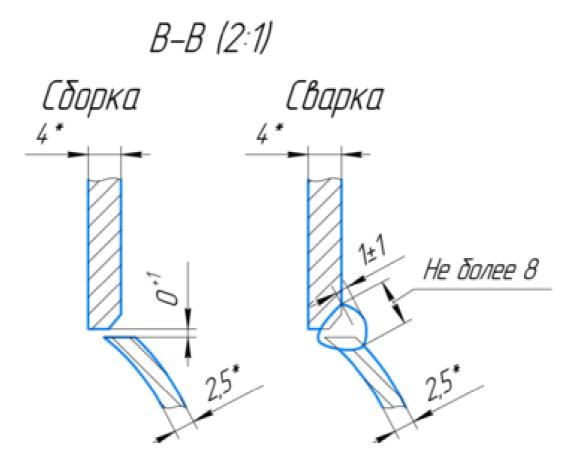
Общий вид шва, соединяющего патрубок (поз. 1) с патрубком (поз. 2)
